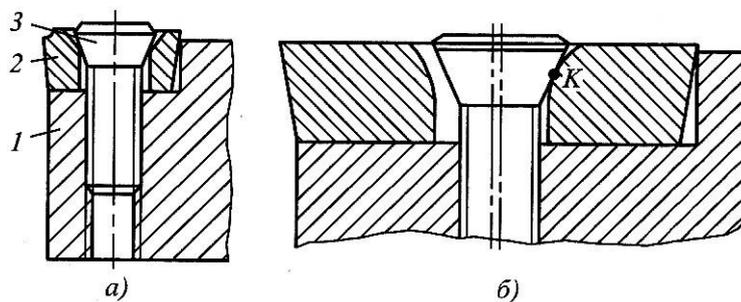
Крепление сменных режущих пластин с центральным фасонным (параболоидным) отверстием винтом (тип S): а) 1 – корпус; 2 – режущая пластина; 3 – крепежный винт; б) схема крепления
